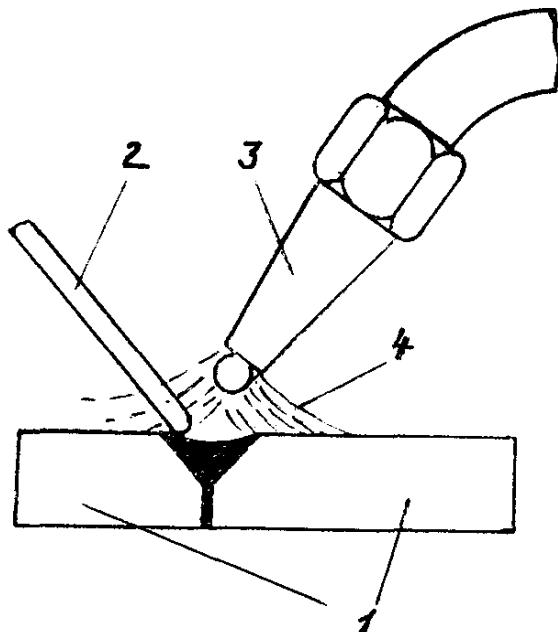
Схема газовой сварки: 1 – свариваемые заготовки; 2 – присадочный металл; 3 – горелка; 4 – газосварочное пламя
